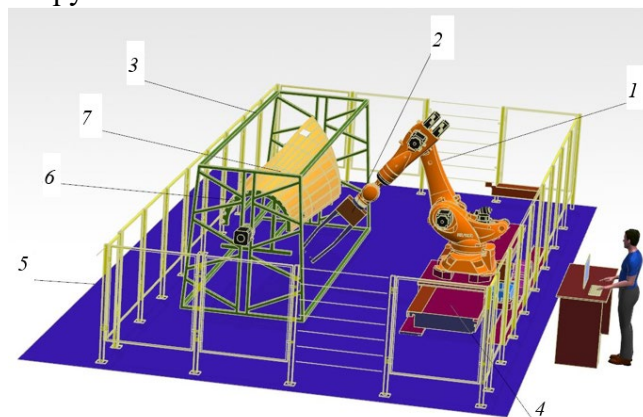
Роботизированная ячейка контактной точечной сварки
